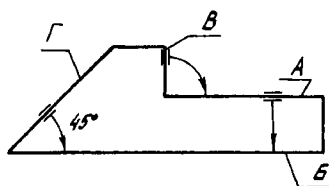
Условные обозначения относительного поворота поверхностей детали
